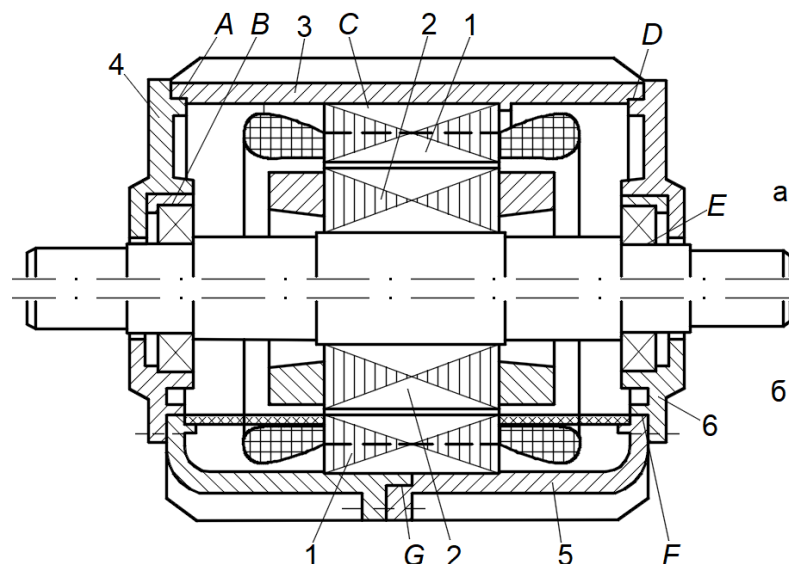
Варіанти конструктивних схем асинхронного двигуна з установкою статора і ротора в підшипникових щитах (*a*) та в двох напівкорпусах з підшипниковими маточинами (*б*): 1 – статор; 2 – ротор; 3 – станина; 4 – щит; 5 – напівкорпус; 6 – маточина.
